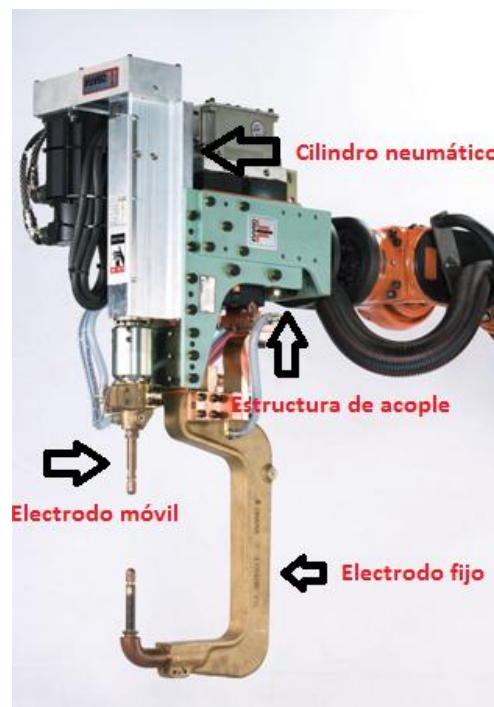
Pinza de soldadura tipo "C" instalada en un robot KUKA (Robot Works, 2016)
